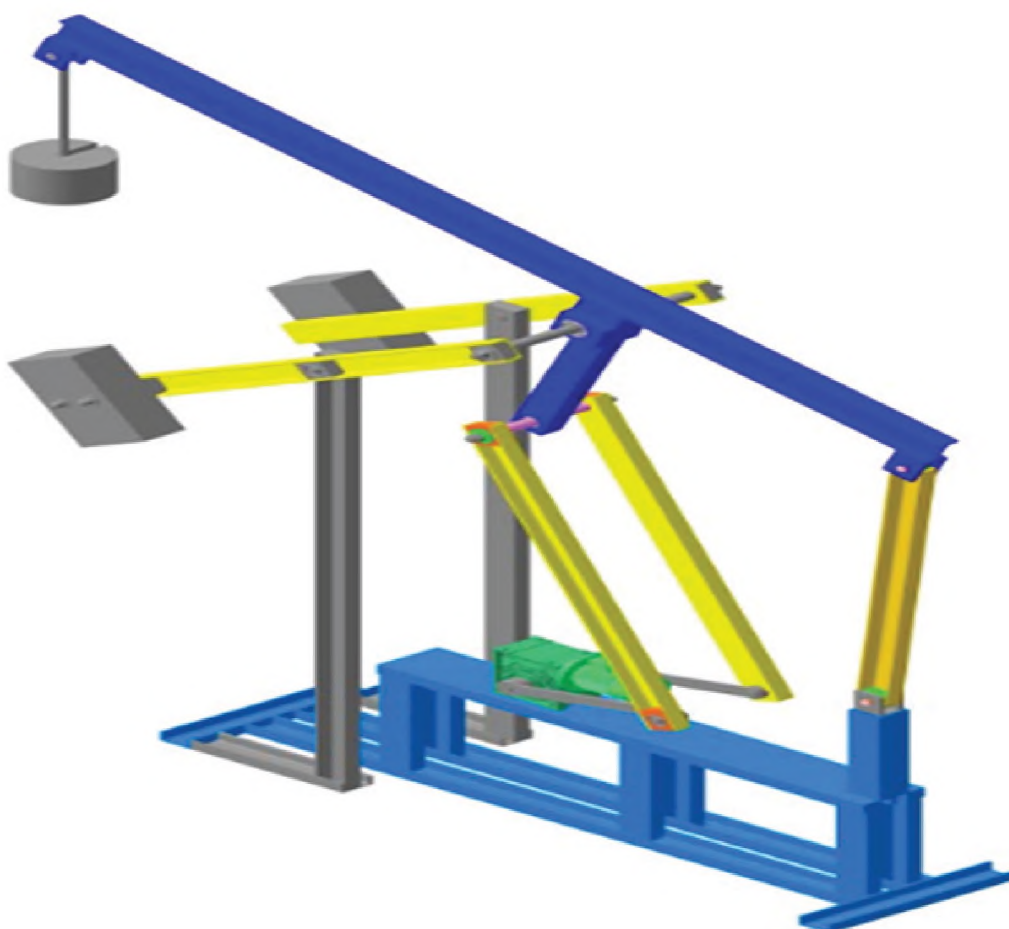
3Д схема механизма привода штанговых насосных установок в верхнем положении
